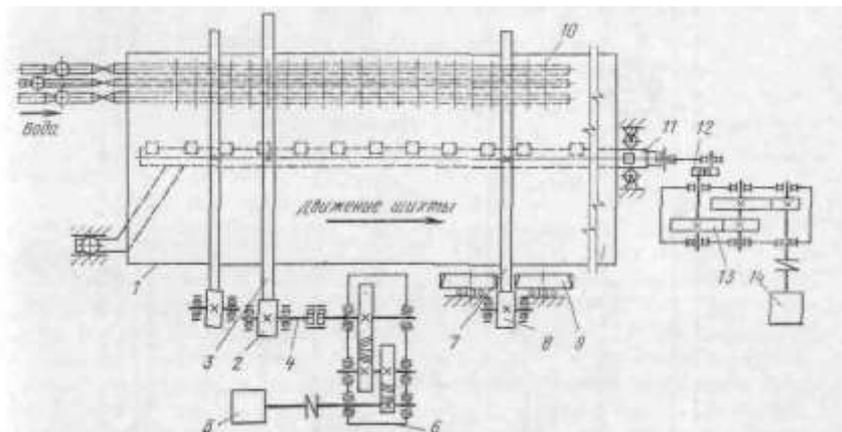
Кинематическая сема привода барабанного смесителя
